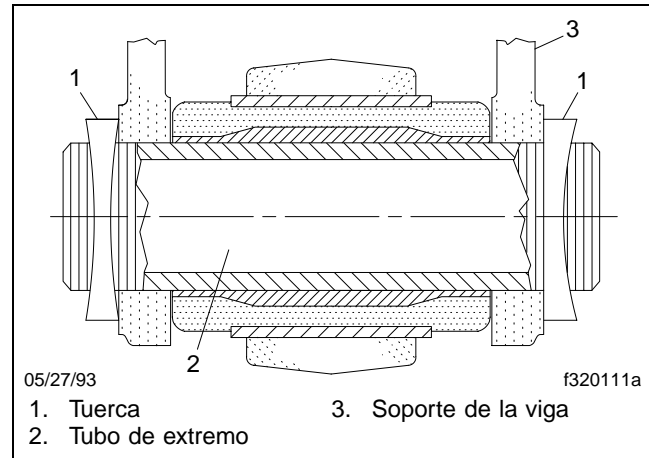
, Conexión tipo adaptador de tres piezas del extremo de la viga
